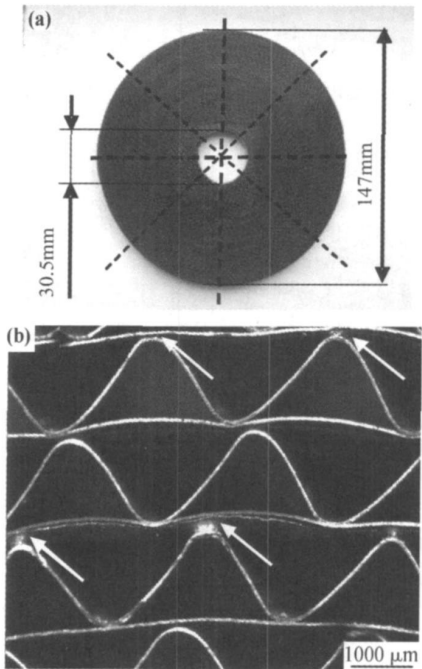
焊后试样外观 (a) 宏观形貌; (b) 钎料润湿情况
